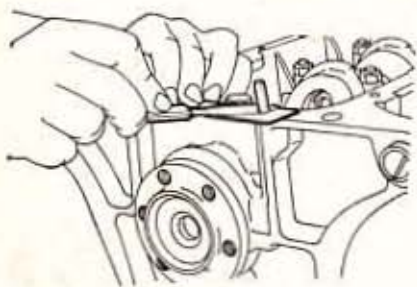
Les joints latéraux doivent dépasser de 0,5 mm
